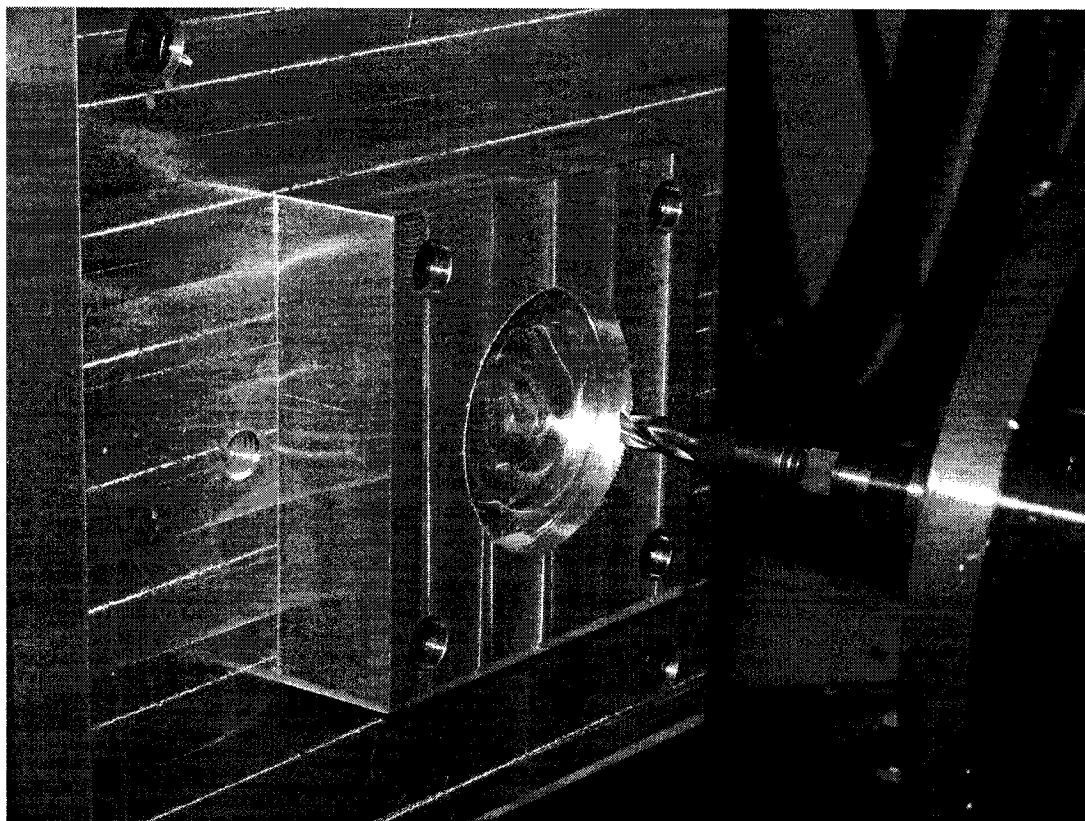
Usinage d'un alésage par fraisage orbital.
